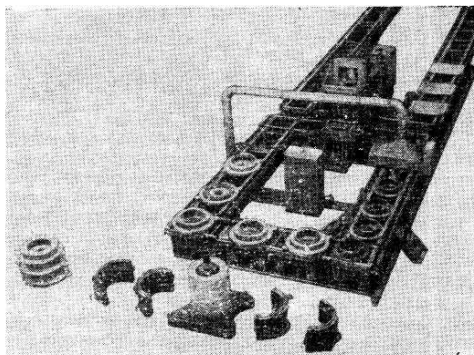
Стержневая линия ЛПО31 и сборочный стенд стержневого блока
